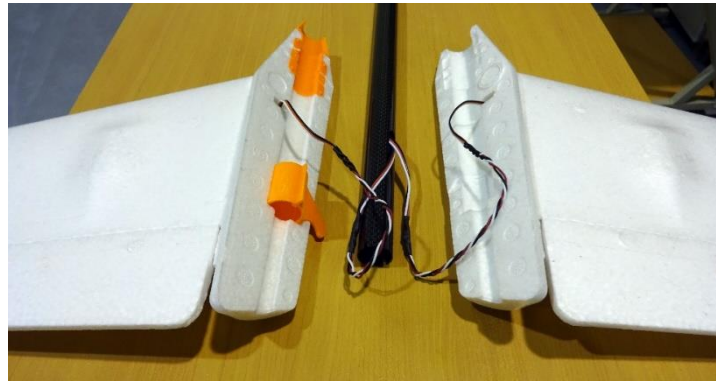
Montaje de la cola, previo al ensamblaje final.
